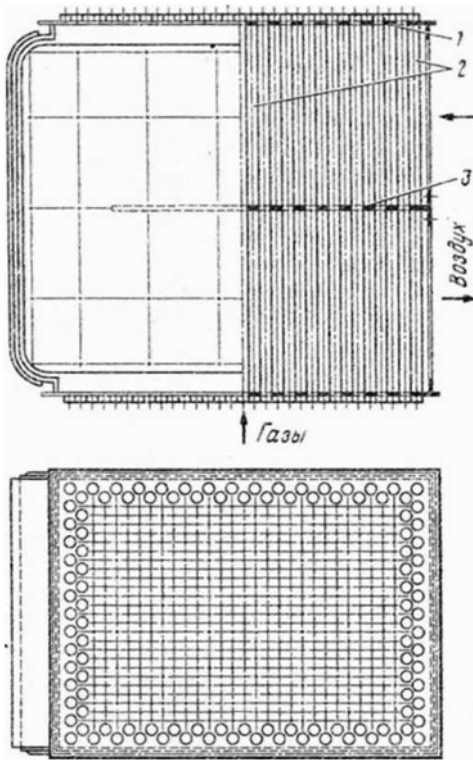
Вертикальный двухходовой трубчатый воздухоподогреватель
